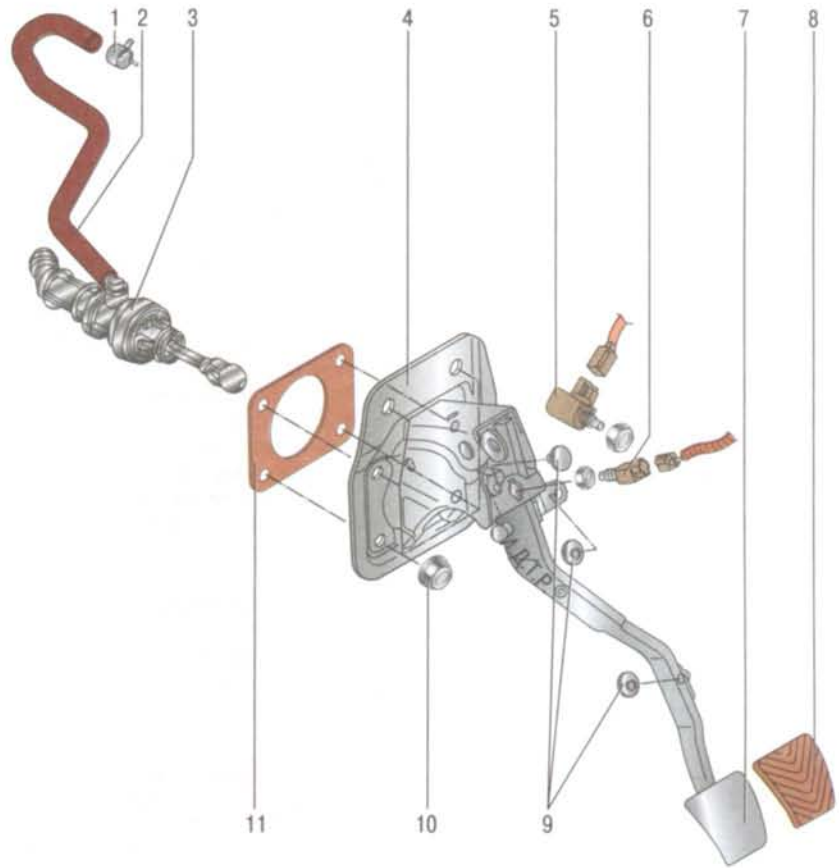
Педаль и главный цилиндр гидропривода выключения сцепления: 1 – хомут крепления шланга подачи тормозной жидкости к главному тормозному цилиндру; 2 – шланг подачи тормозной жидкости к главному тормозному цилиндру от бачка; 3 – главный цилиндр привода выключения сцепления; 4 – кронштейн педали сцепления; 5 – датчик выключения сцепления; 6 – выключатель круиз-контроля; 7 – педаль сцепления; 8 – накладка педали сцепления; 9 – упоры; 10 – гайка крепления кронштейна педали сцепления; 11 – прокладка
